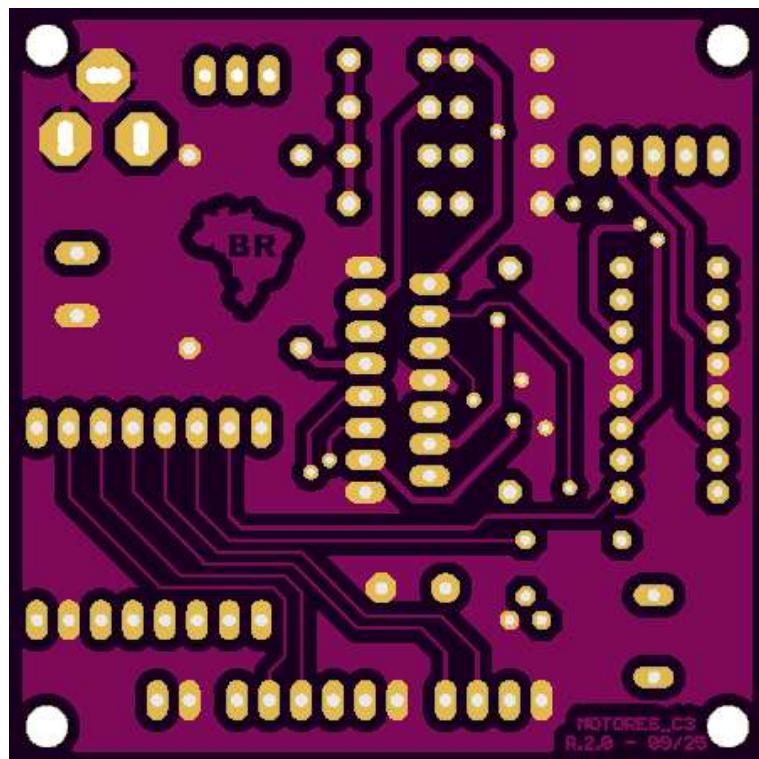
Placa MOTORES\_C3 rev. 2.1 (lado da solda)
